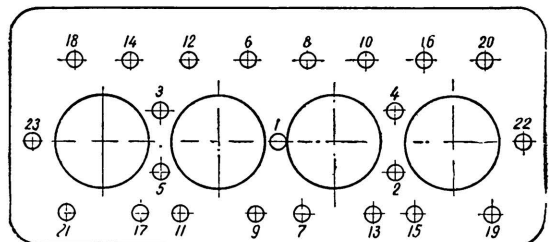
Схема последовательности затяжки гаек шпилек крепления головки блока цилиндров
